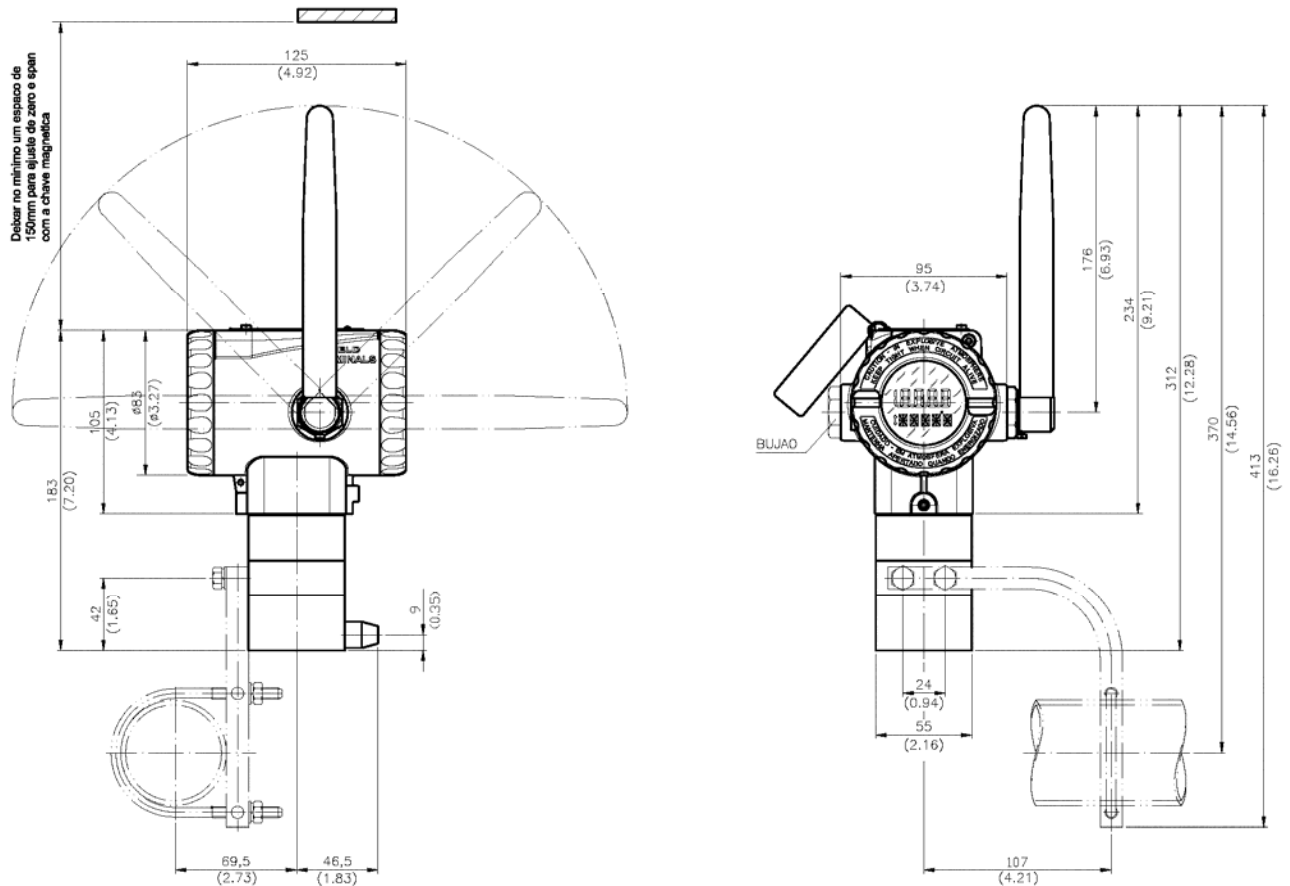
Desenho Dimensional de Montagem do TP400 WirelessHART™ na vertical
